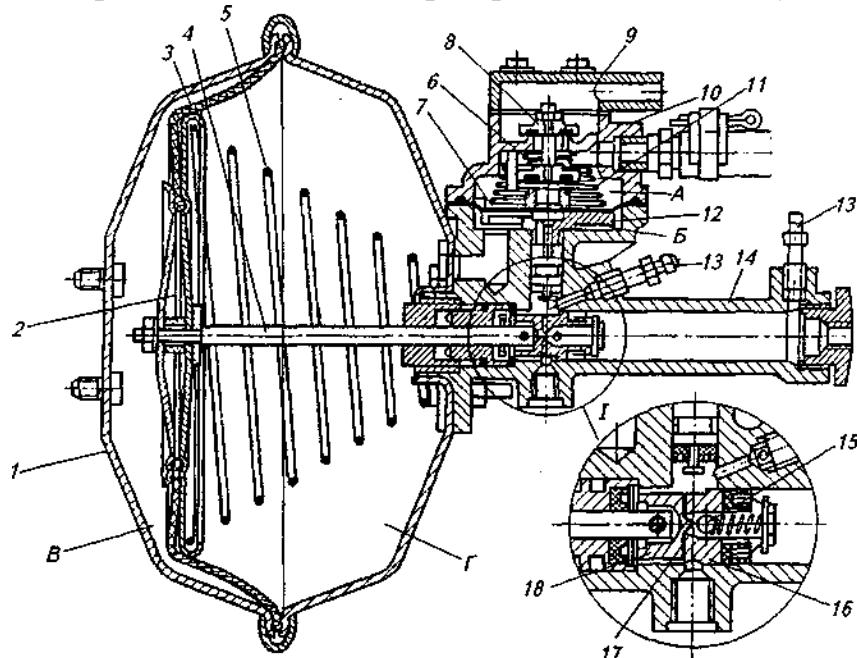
Гидровакуумный усилитель тормозов: А, Б — полости клапана управления; В, Г— полости камеры; 1 — камера усилителя; 2— тарелка диафрагмы; 3 — диафрагма усилителя; 4— толкатель поршня; 5— пружина диафрагмы; 6— вакуумный клапан; 7— диафрагма клапана управления; 8—воздушный клапан; 9—
